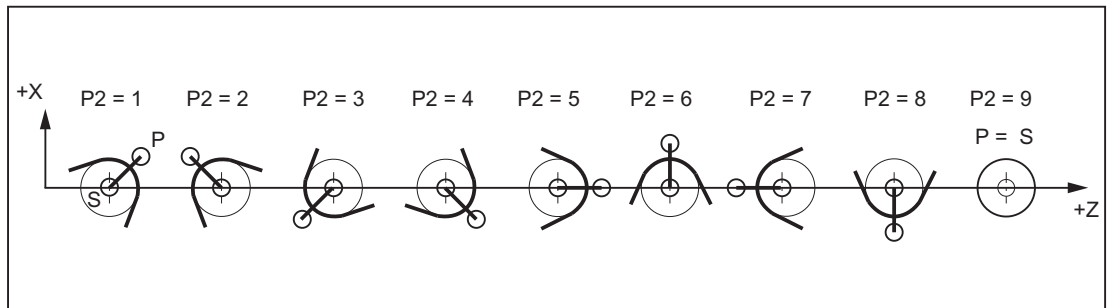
刀具参数 2 (P2)：在车削中心后侧加工时
